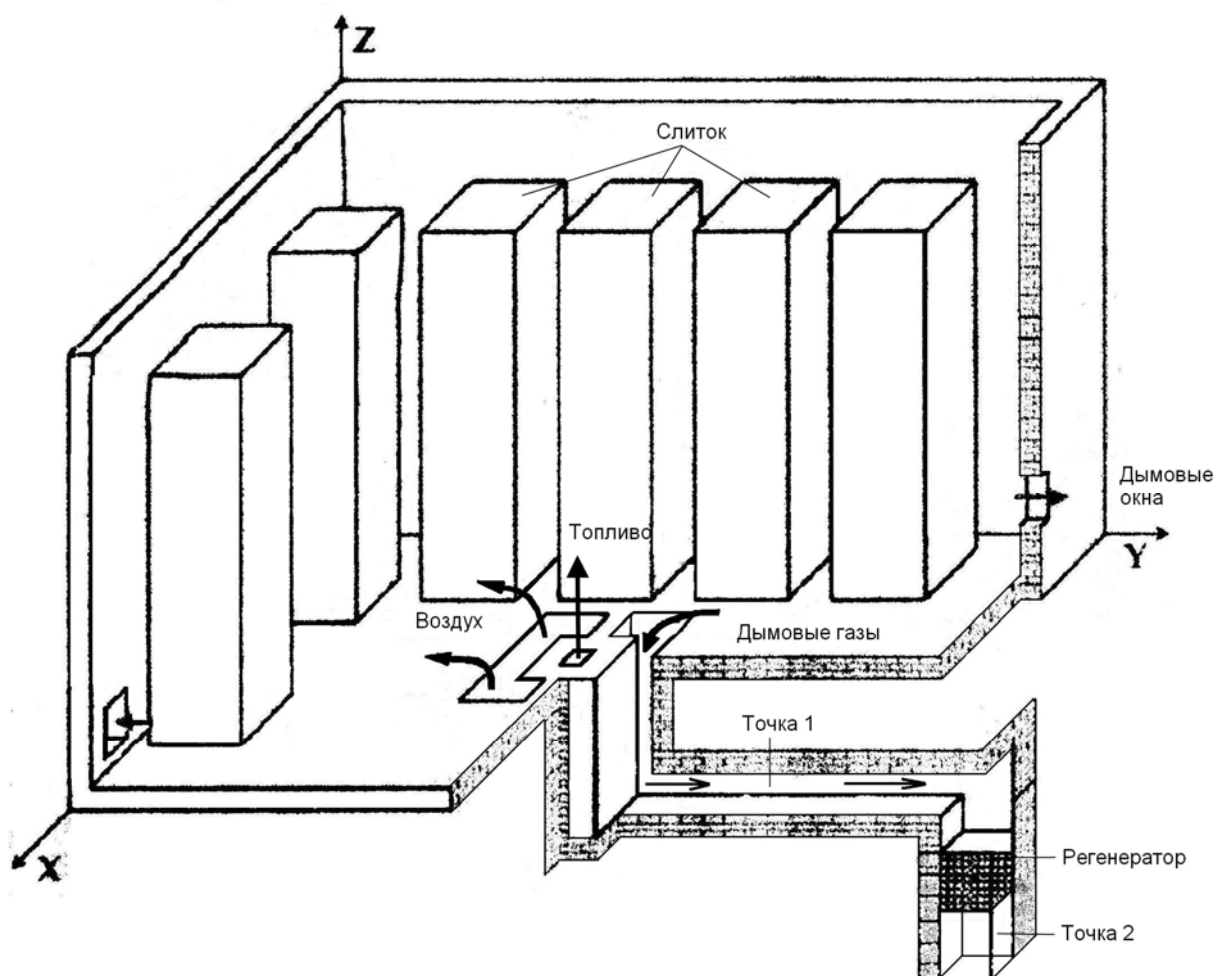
Нагревательный колодец с отоплением из центра пода
